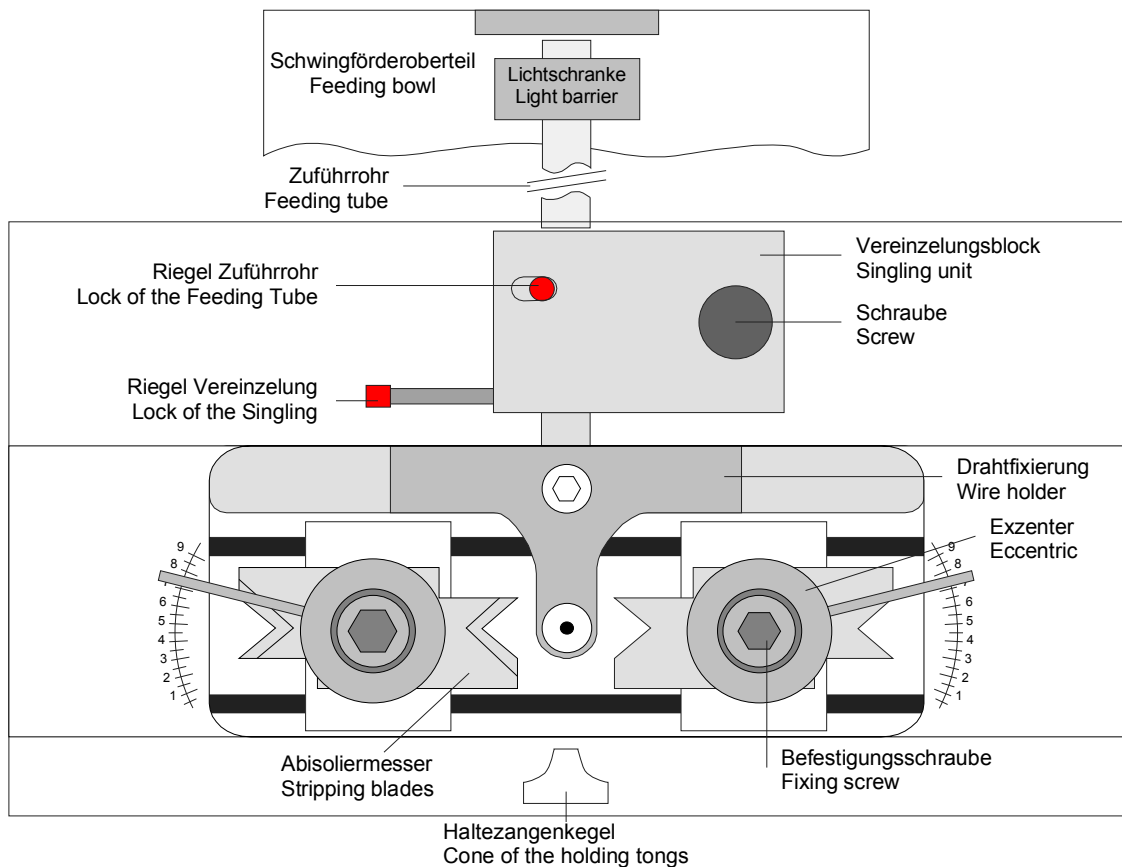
Innenansicht mit Abisoliereinheit / Interior view with stripping unit
